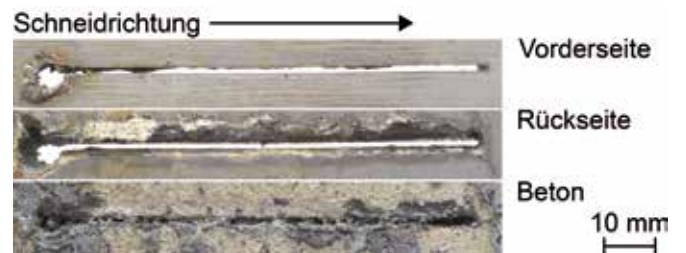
Schnitt eines mit Beton hinterfüllten 10 mm starken Bleches
